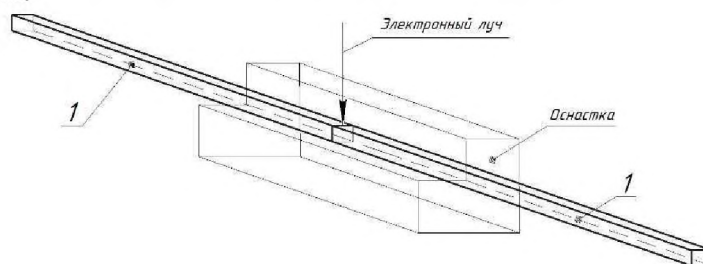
Схема сварки ЭЛС: 1 – свариваемые образцы
